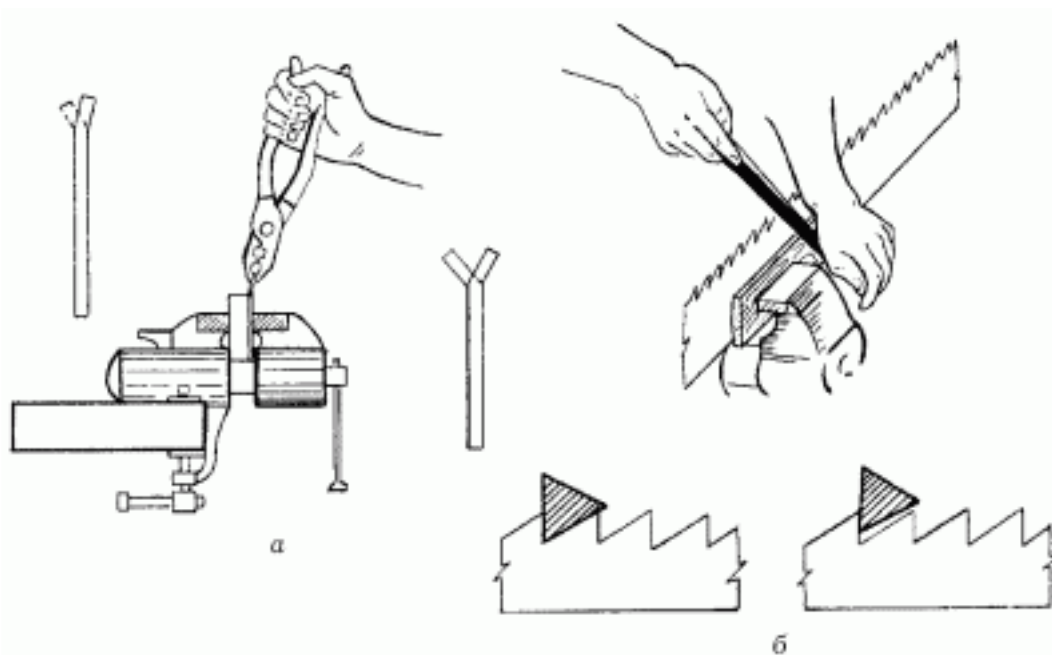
Подготовка пилы к работе: а – развод зубьев; б – заточка.
